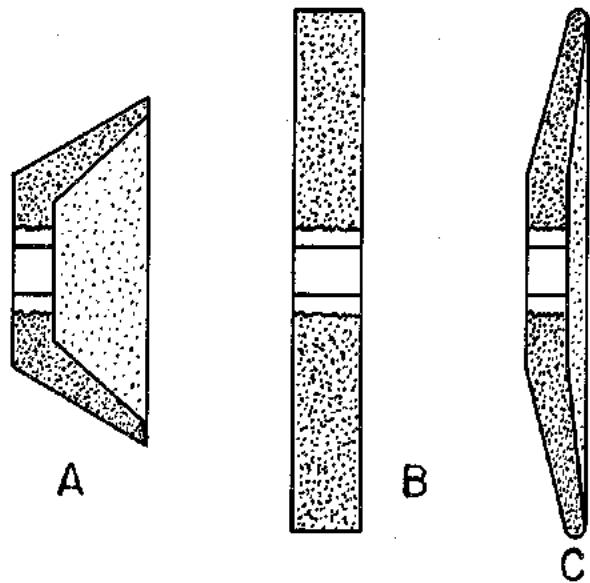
Muelas para rectificar fresas: (A) de copa; (B) de disco; (C) de plato.
